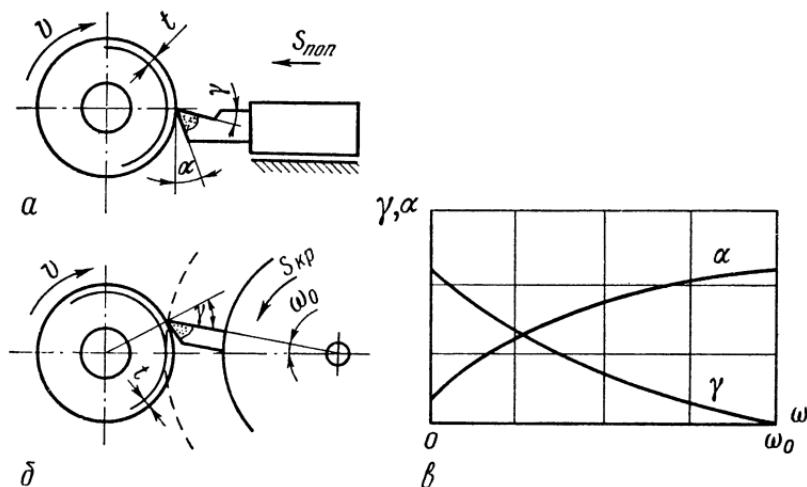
Схемы токарной обработки наружных цилиндрических поверхностей
